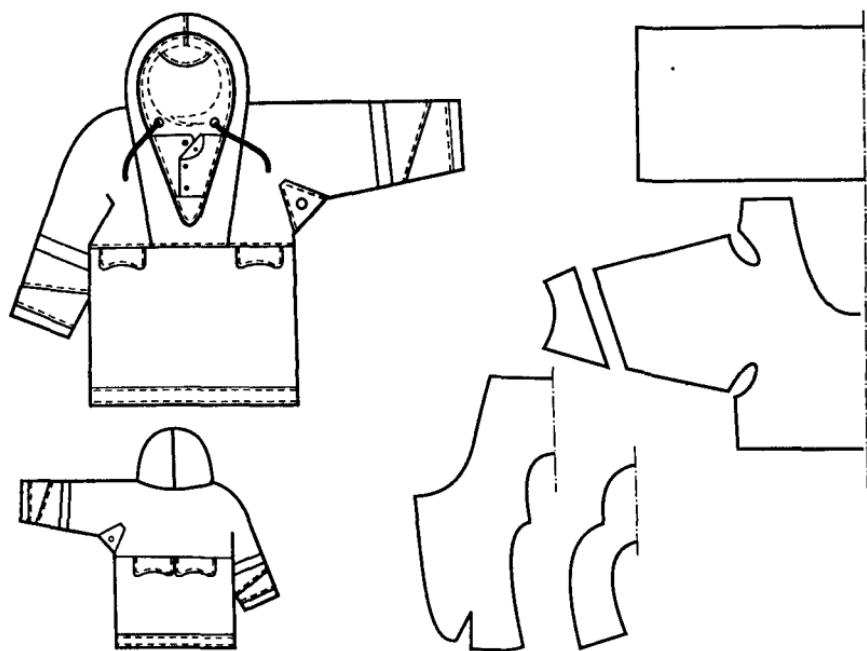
Внешний вид и схема конструктивного решения верхней части костюма для рыбаков
